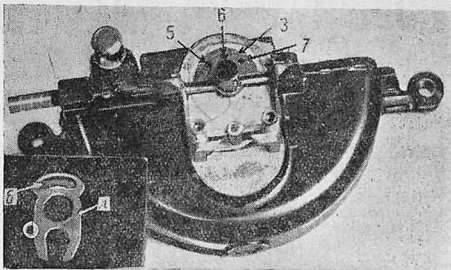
Общий вид стеклоочистителя с раскрытой золотниковой коробкой
